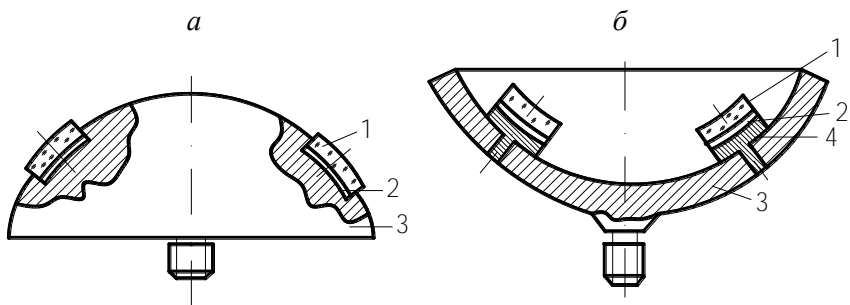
Схема блокировки заготовок линз на клеечном приспособлении:
